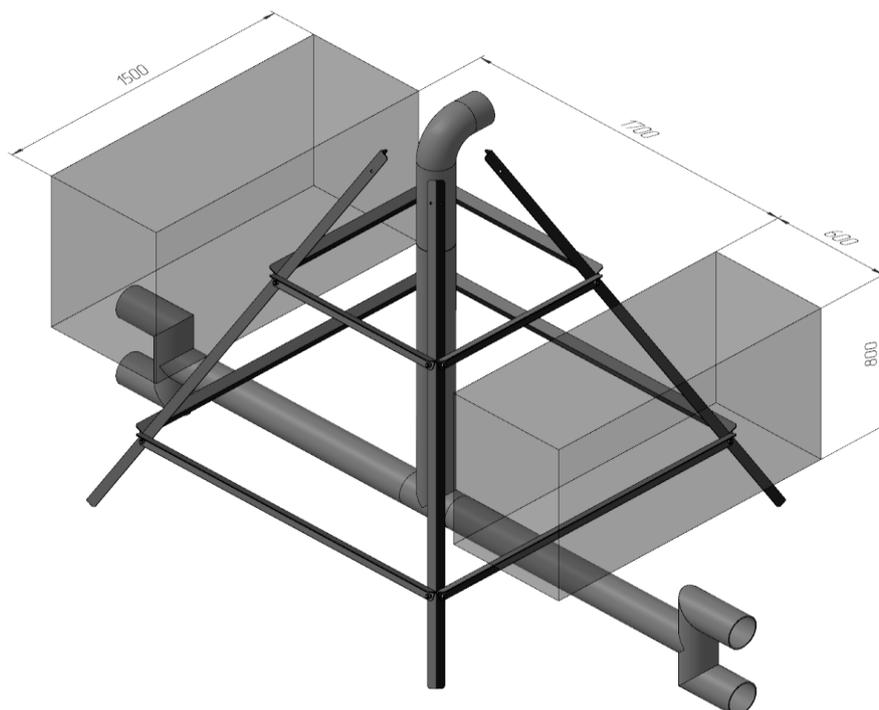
Схема главной ходовой тележки с центральным размещением вертикального сегмента водоподводящего трубопровода дождевальная машины
